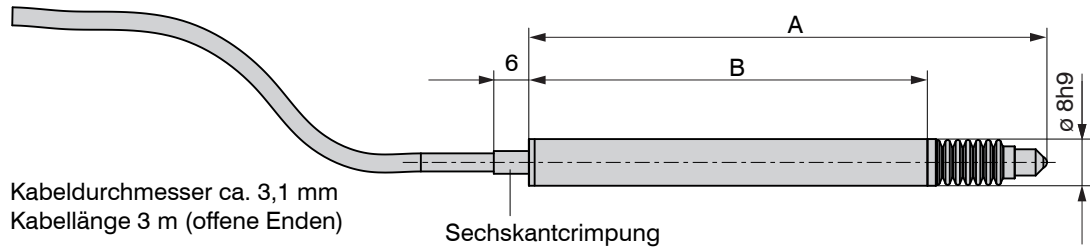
Gehäusemaße für Messtaster DTA-xG8-3-CA
